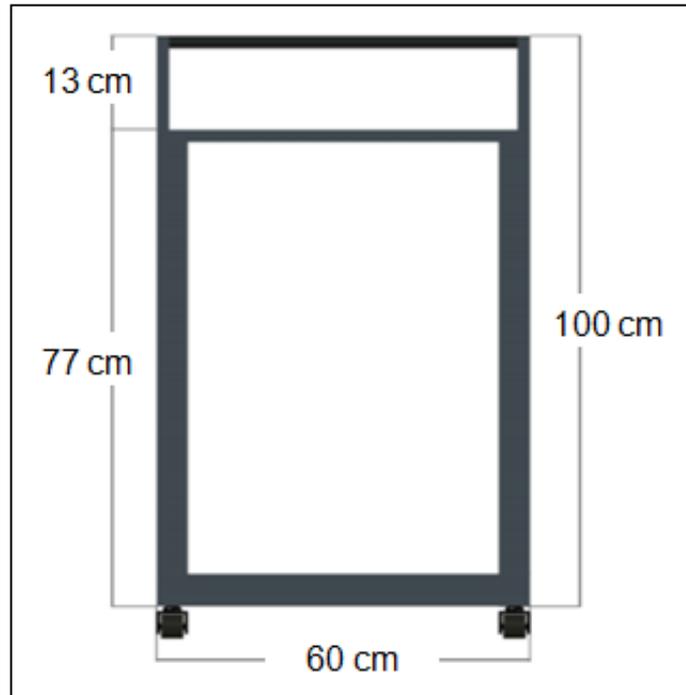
Dimensiones de la Estructura 2 - Vista frontal
